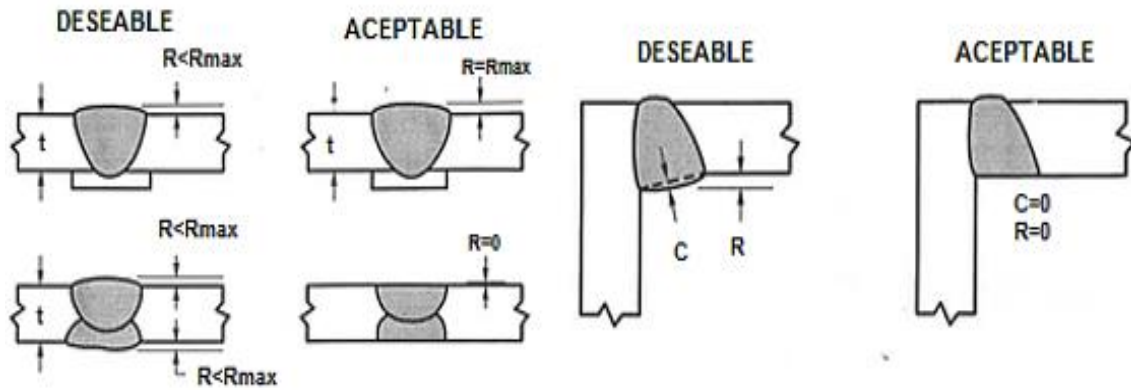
Tamaños y Perfiles de soldaduras
